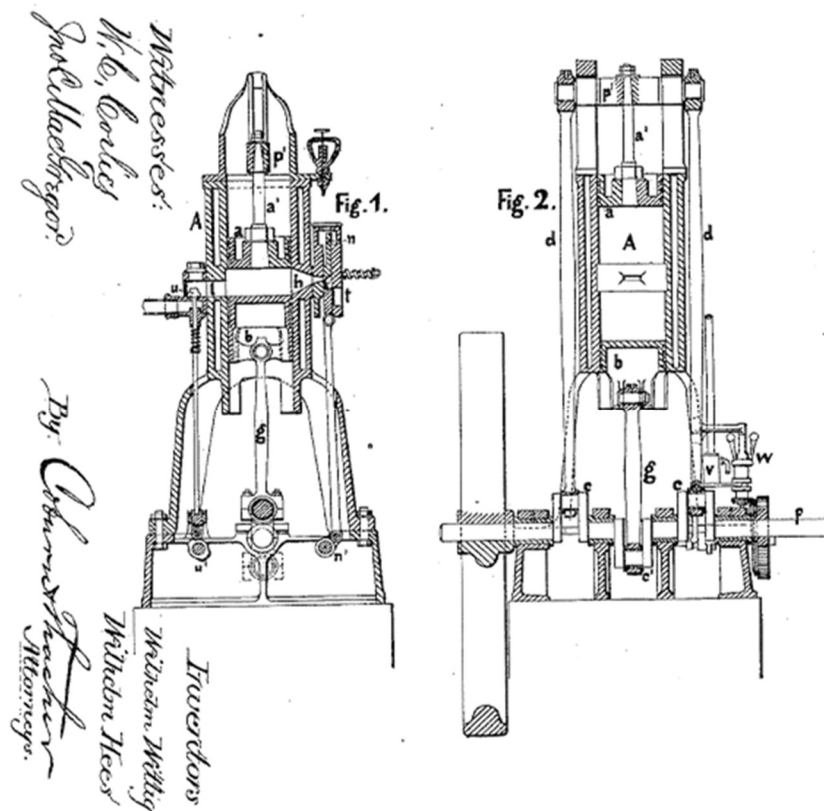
Motor OP de cambota única de Wittig. Wittig e Hees (1879)
